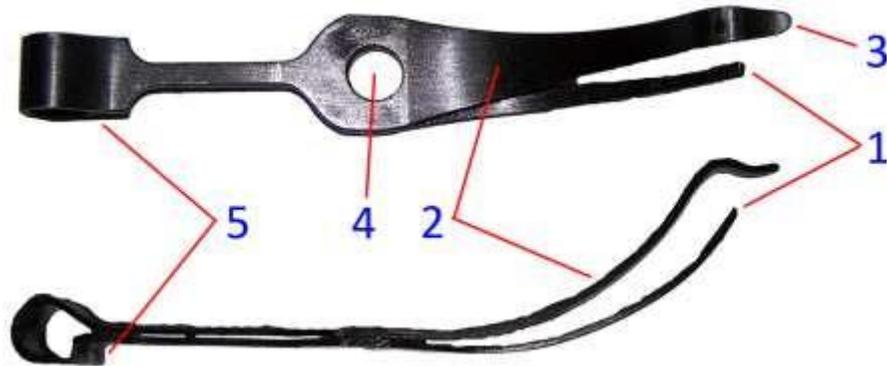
Бойова пружина (вигляд з торця і вигляд з боку):
